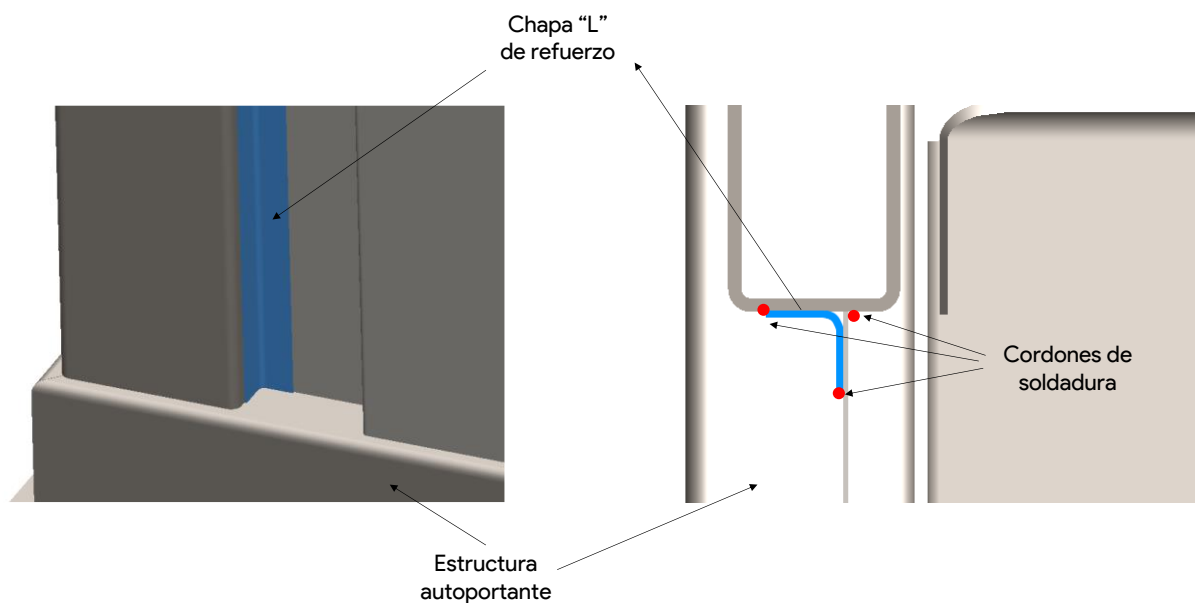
Chapa "L" de refuerzo y cordones de soldadura.
